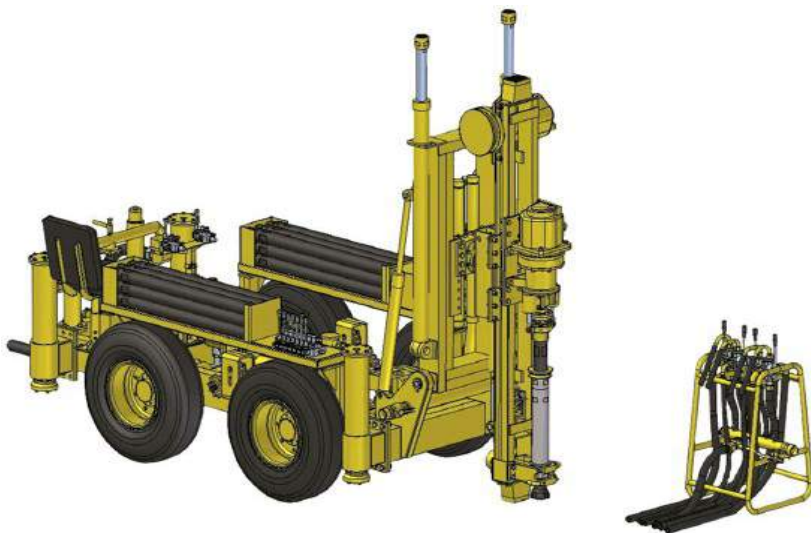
Общий вид самоходного бурового станка БП-100С
